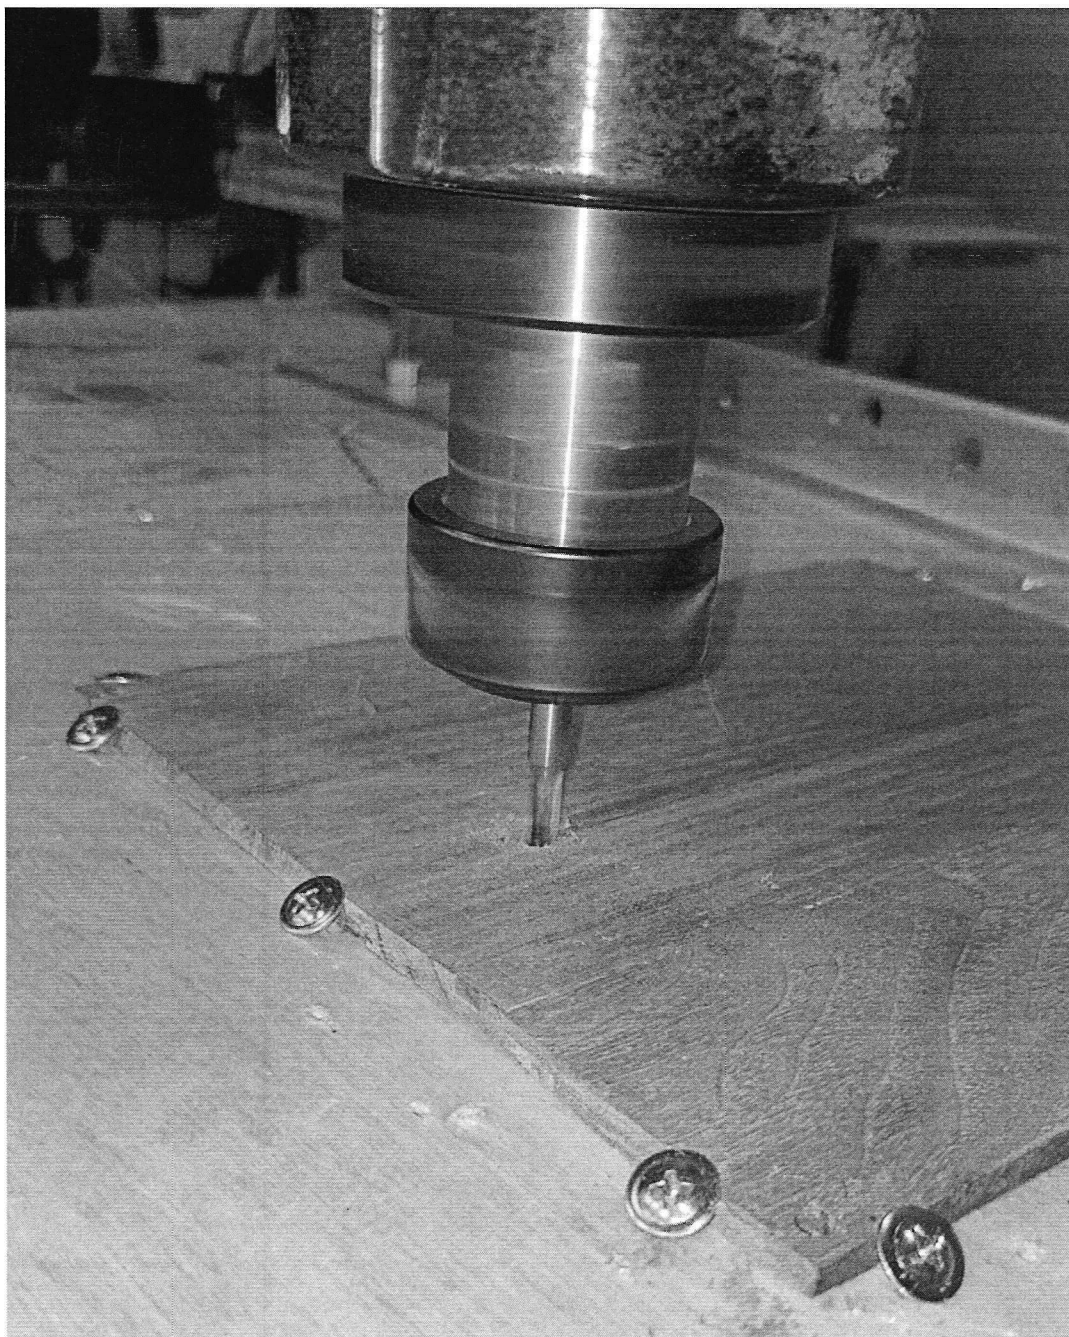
Процесс фрезеровки ламелей из Американского ореха
